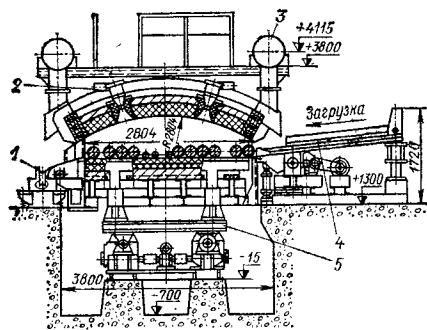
Печь для нагрева металла перед резкой с подъемно-шагающими балками
